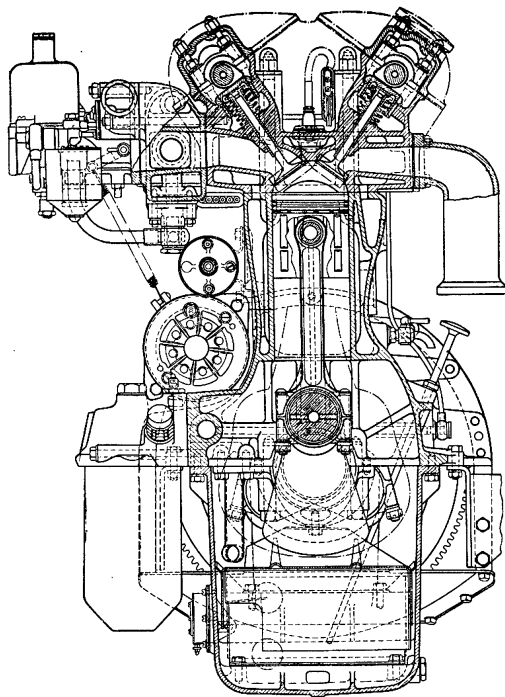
Поперечный разрез двигателя автомобиля «Ягуар» XK-120
